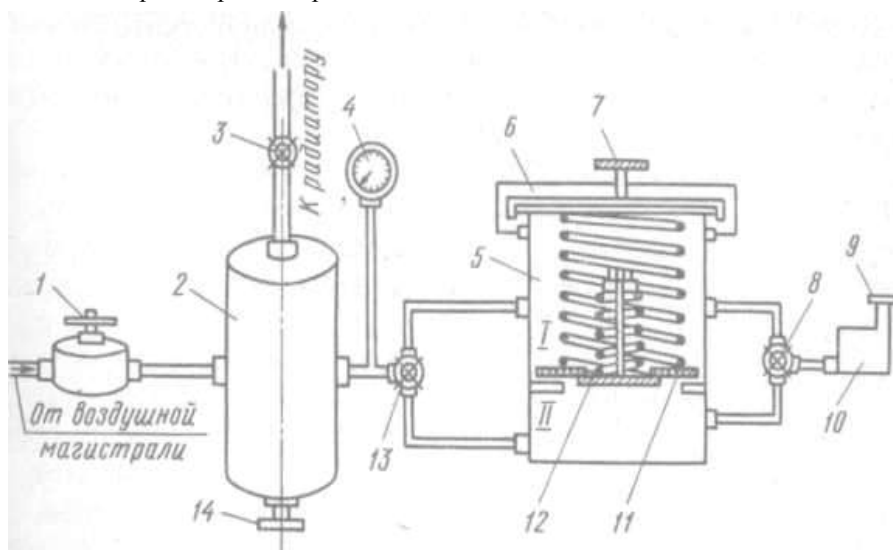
Схема приспособления для проверки клапанов пробки радиатора и герметичности системы охлаждения двигателя
